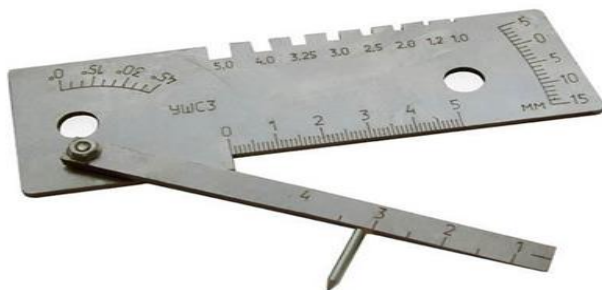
«Универсальный шаблон сварщика» (УШСЗ)
